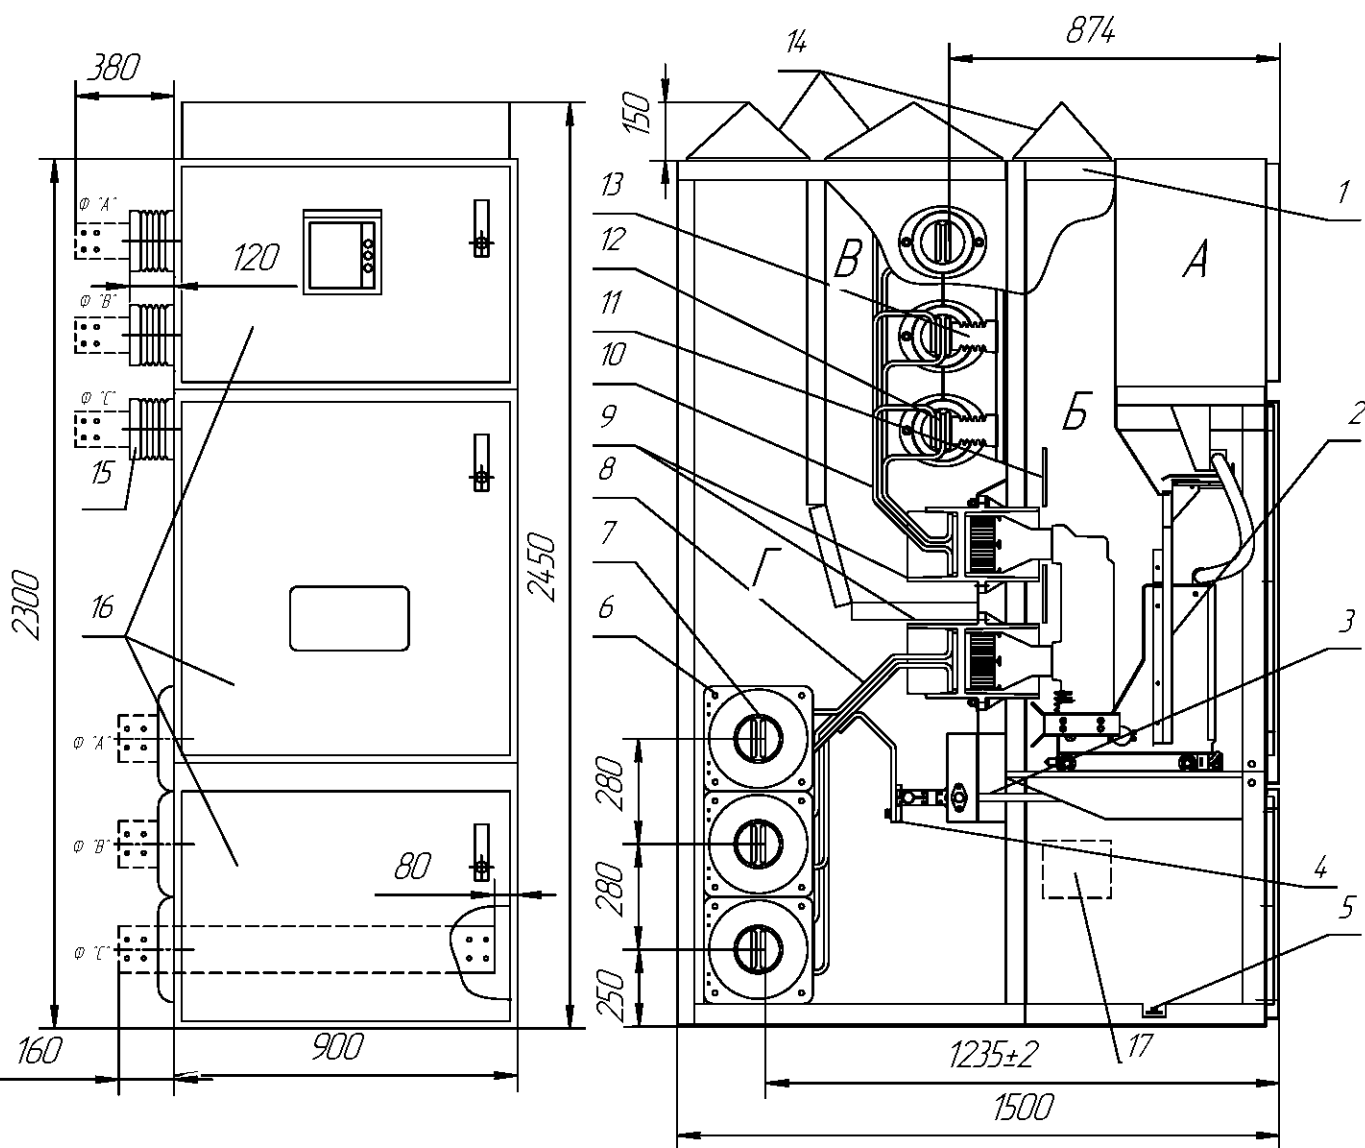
Габаритные, установочные, соединительные размеры шкафов
